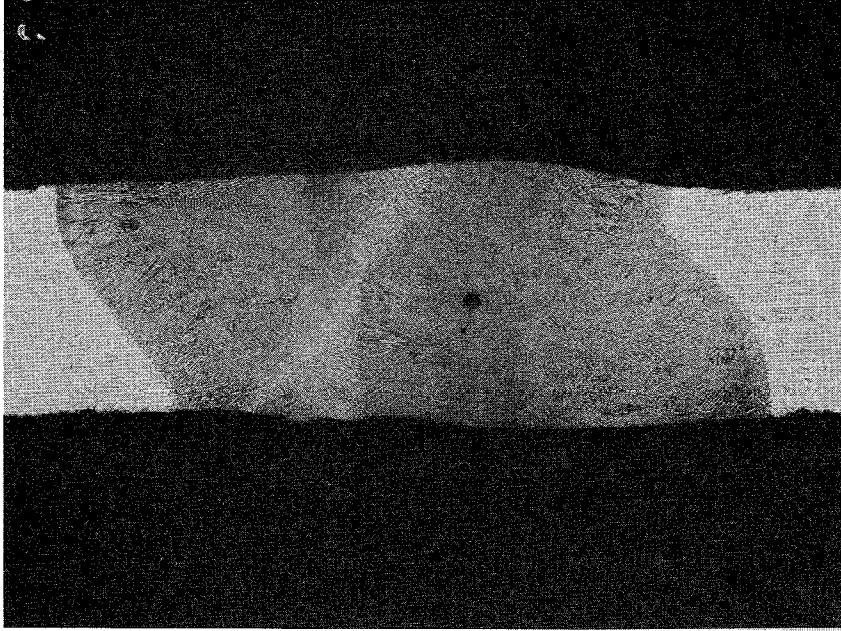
Makroaufnahme vom Querschliff der Schweißnaht bei dem Cr-Ni-Stahl 1.4539 im WS-Zustand (Bindefehler aufgrund nicht entfernter Zunderschichten nach der Wärmebehandlung) $V = 10:1$
